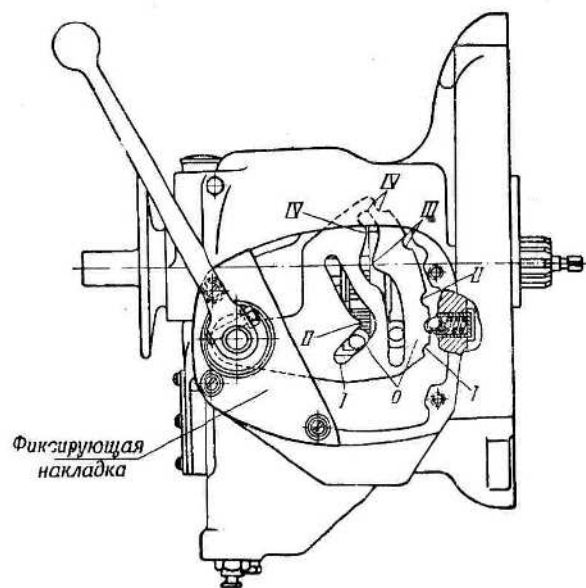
Регулировка коробки передач М-76 со снятой крышкой
